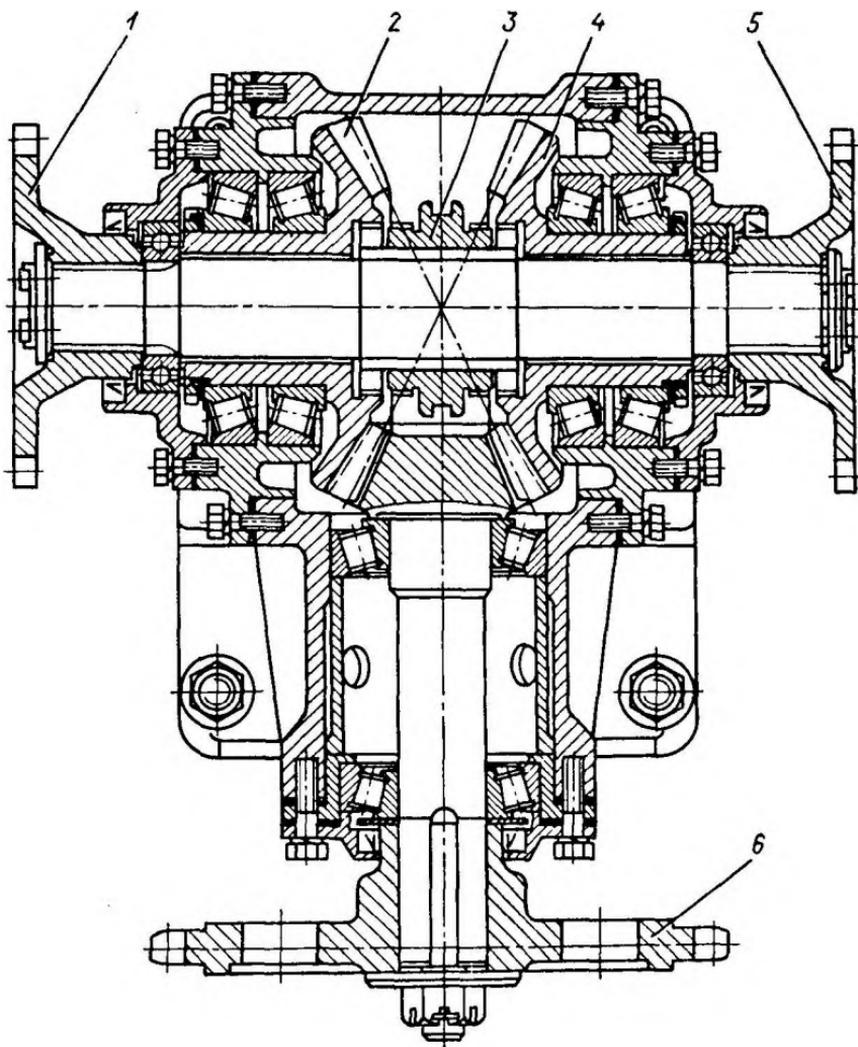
Редуктор привода конвейера экскаватора ЭР-7АМ
